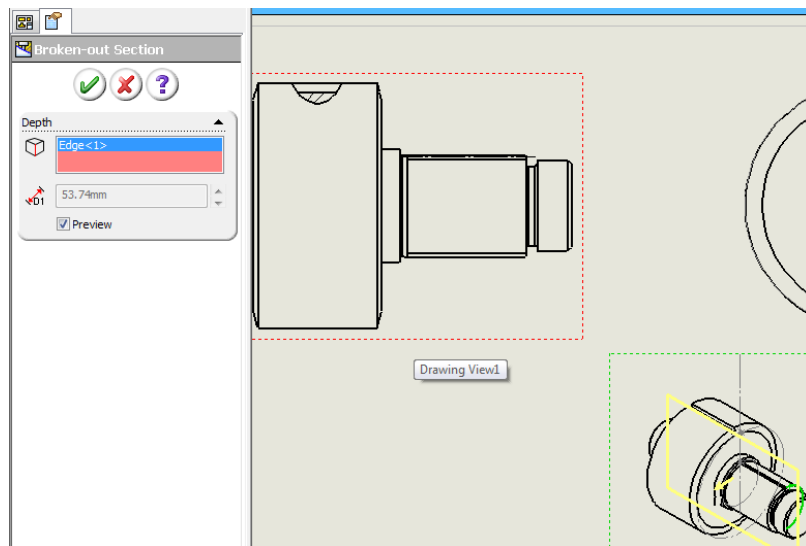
Налаштування інструменту ВЫНУТЫЙ РАЗРЕЗ (Broken-Out section)
